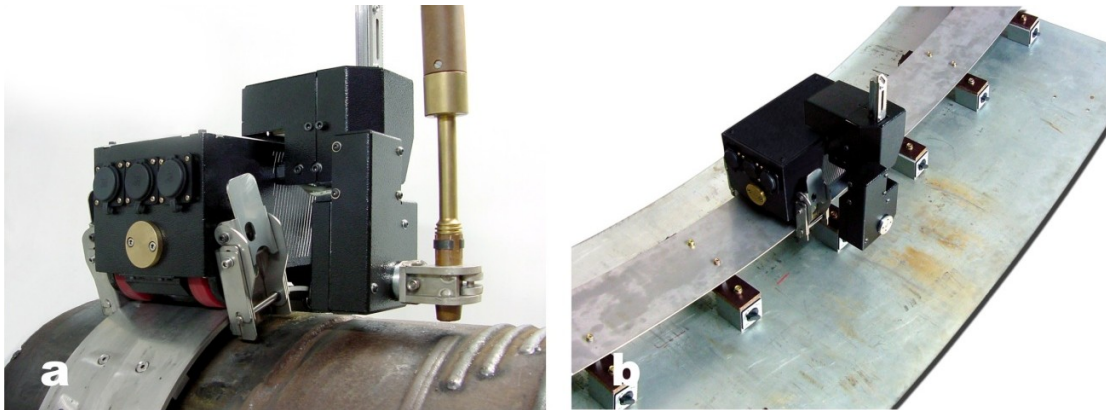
Em (a) montagem para soldagem orbital e em (b) para a soldagem de superfícies curvas
